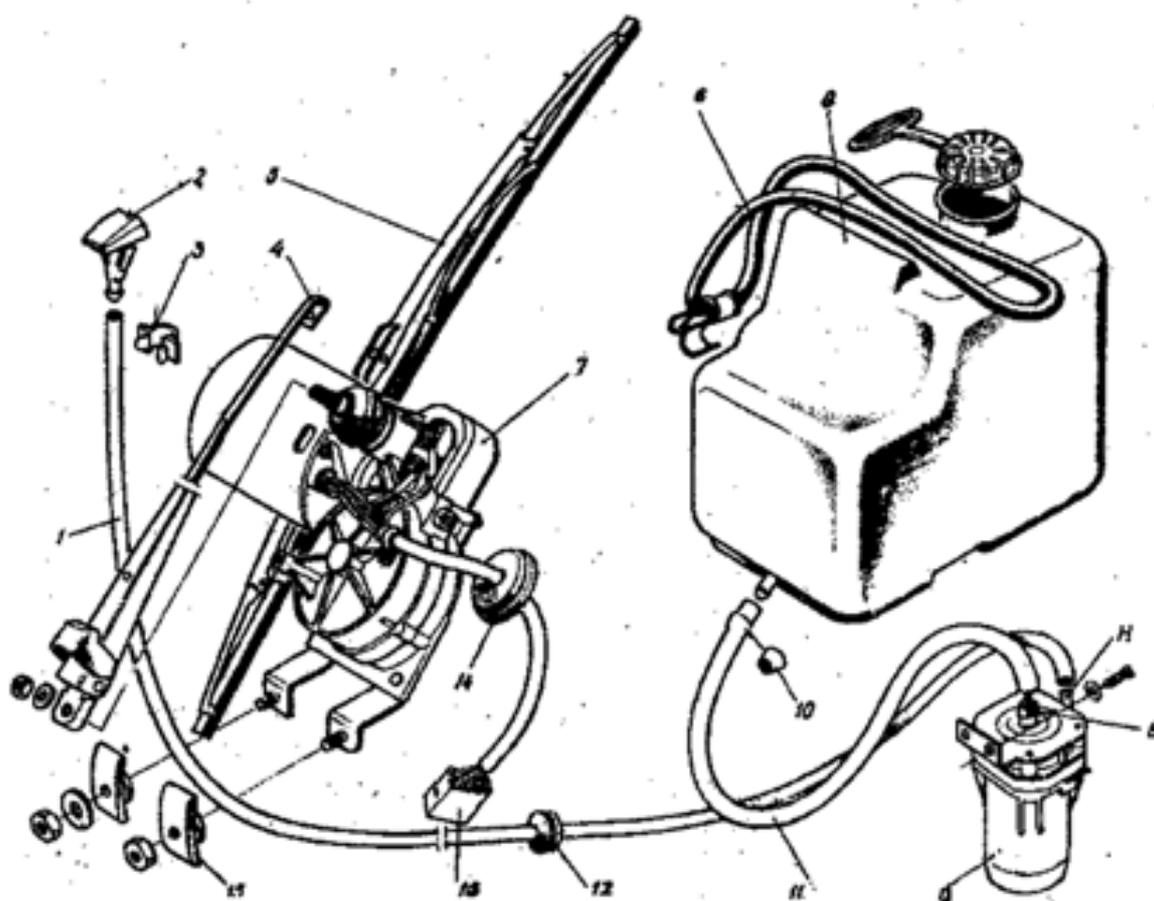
Стеклоочиститель и стеклоомыватель ветрового окна: 1 - шланг жиклера; 2 - жиклер в сборе; 3 - скоба крепления шланга; 4 - рычаг; 5 - щетка; 6 - держатель бачка; 7 - моторедуктор ветрового стекла; 8 - бачок; 9 - мотонасос; 10 - фильтр; 11 - шланг бачка; 12, 14 - втулка уплотнительная; 13 - штеккерные кодыжки; 15 - втулка дистанционная
